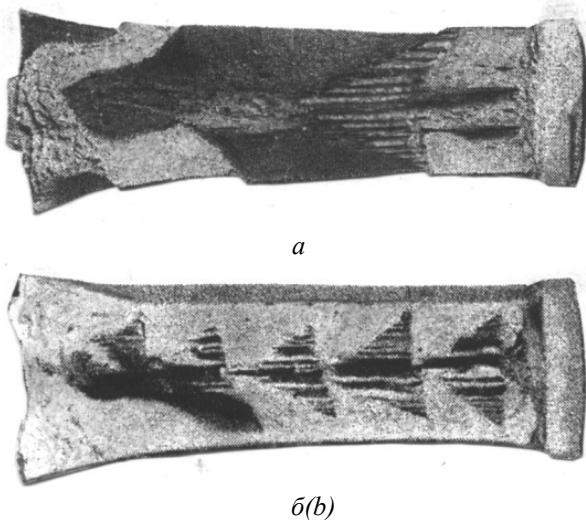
Зоны в виде «размерной стрелки» в изломе стали X70 контролируемой прокатки : а – единственный участок; б – чередующиеся участки / Fig. 3. The zone of «arrowhead» destruction in the DWTT specimen fracture of steel X70 : a – the single area; b – alternate areas
